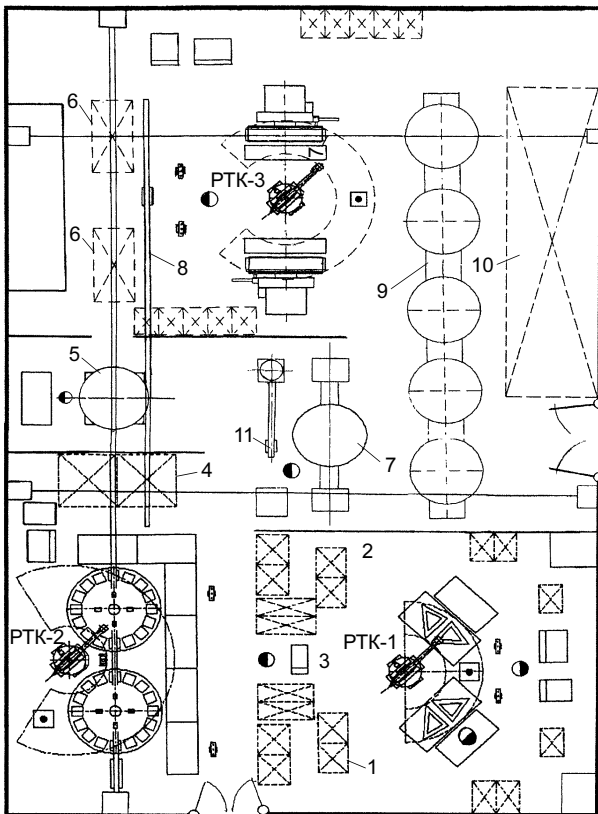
Схема участка роботизированной сварки барабана жатки
